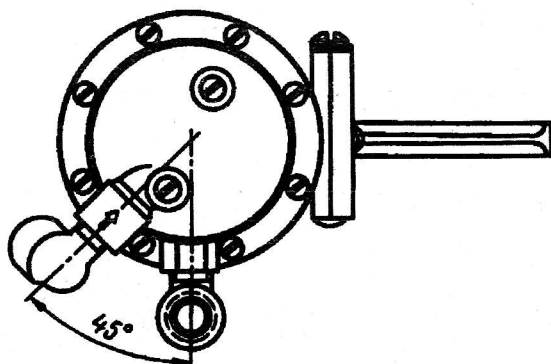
Положение головки и крышки топливного насоса относительно корпуса
